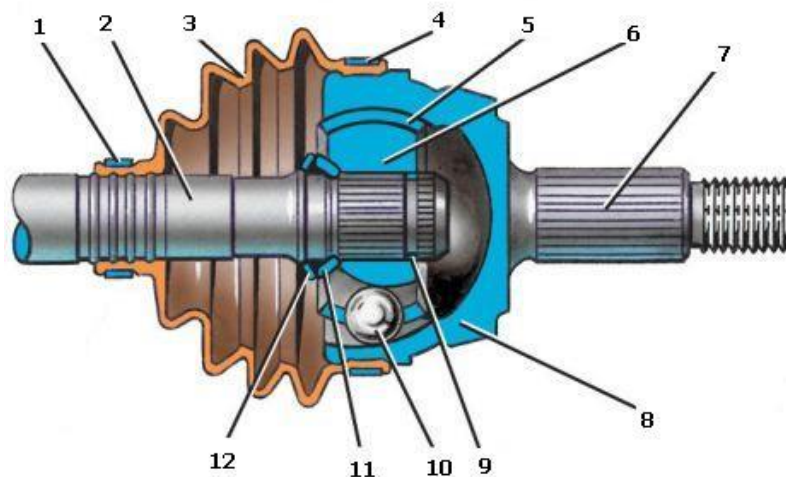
Схема шарнира равных угловых скоростей [6]:
